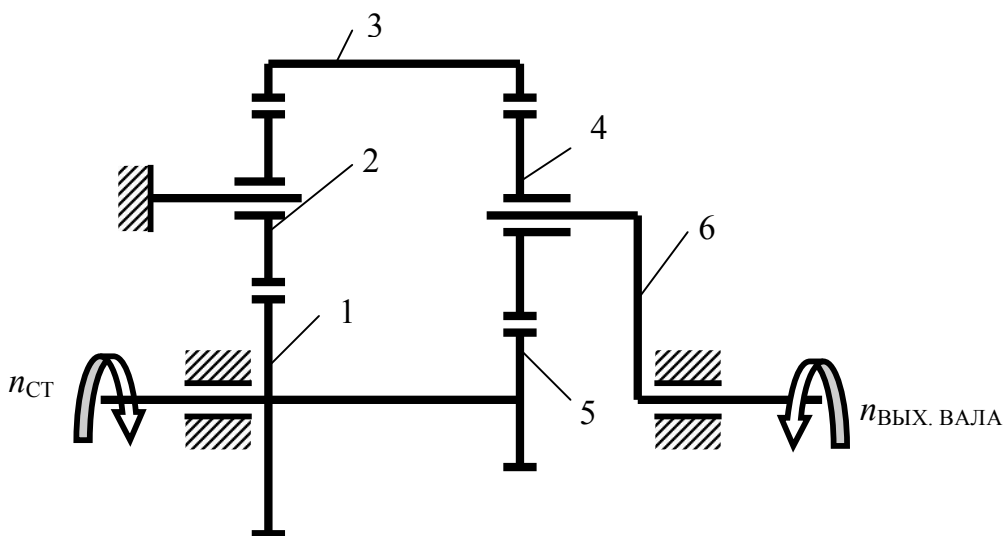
Кинематическая схема редуктора: 1 – большая центральная шестерня; 2 – паразитная шестерня; 3 – зубчатый венец; 4 – сателлит; 5 – малая центральная шестерня; 6 – водило
